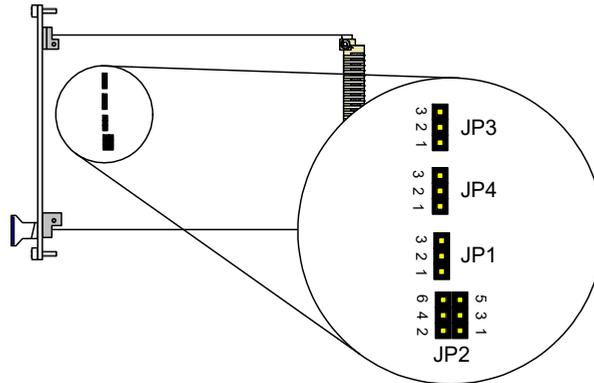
Lage und Bezeichnung der Steckbrücken auf dem Board
